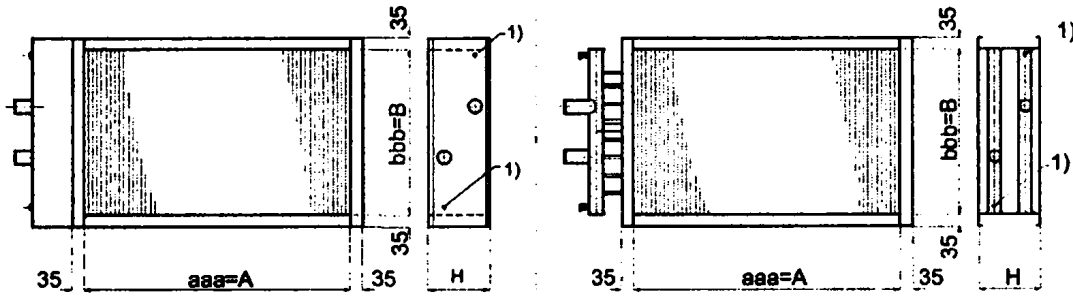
Габаритные размеры воздухоохлаждателей ВНВ243 с фронтальными сечениями расширенного типоразмерного ряда
